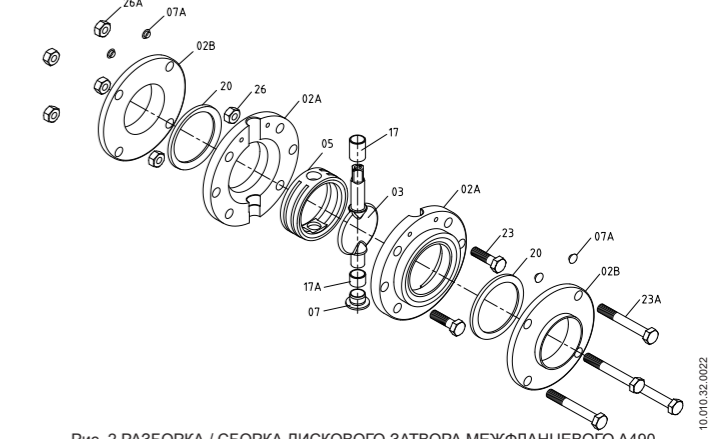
РАЗБОРКА / СБОРКА ДИСКОВОГО ЗАТВОРА МЕЖФЛАНЦЕВОГО A490
